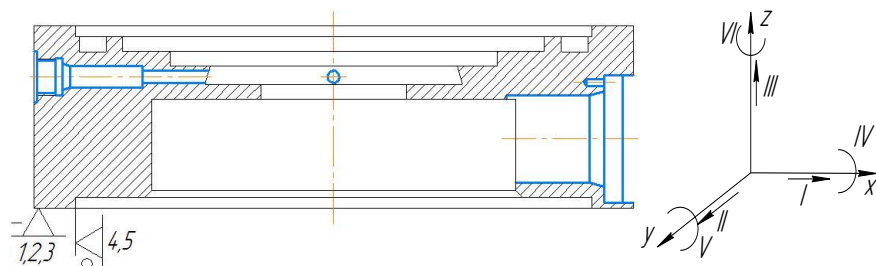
Схема базування заготовки на Багатоцільовій з ЧПУ операції
